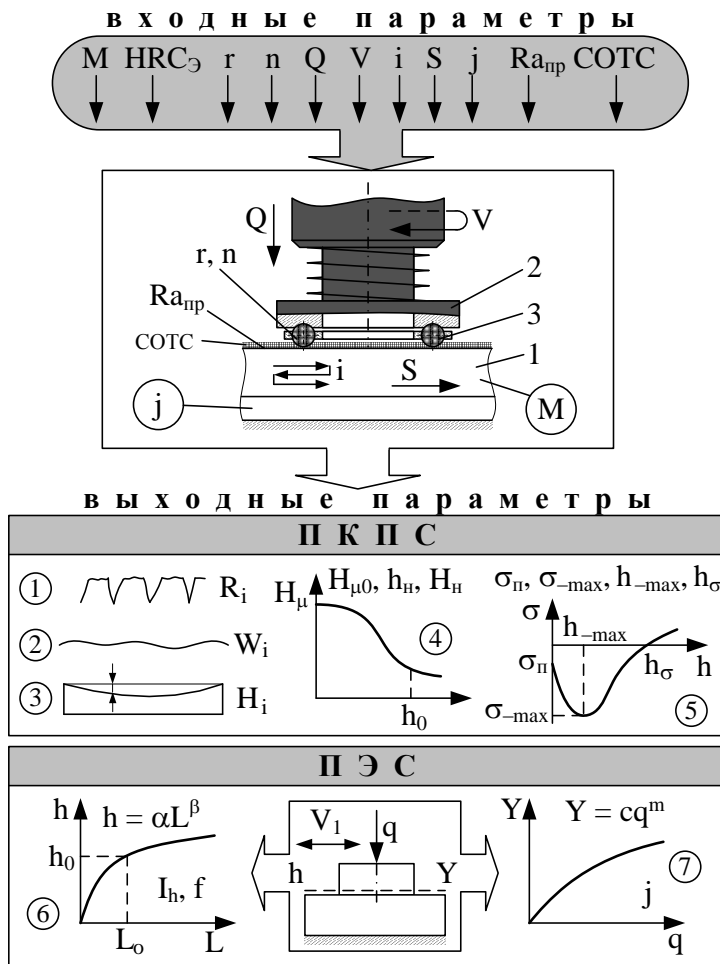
Схема процесса обработки методом ППД шариковой головкой: 1 – обрабатываемая деталь, 2 – шариковая головка, 3 – деформирующий элемент
